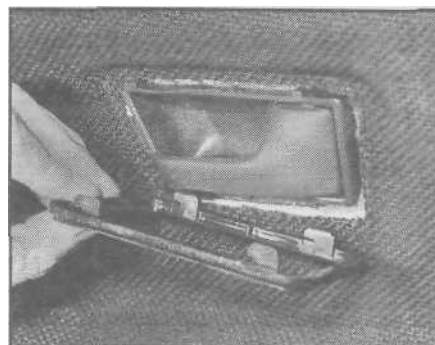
Детали замка крышки багажника [Jetta]
